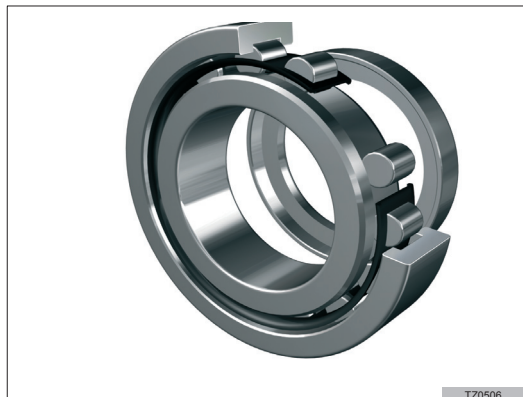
walcowe, poprzeczne, 1-rzędowe, bez pierścienia wewnętrznego - typ RNU..
